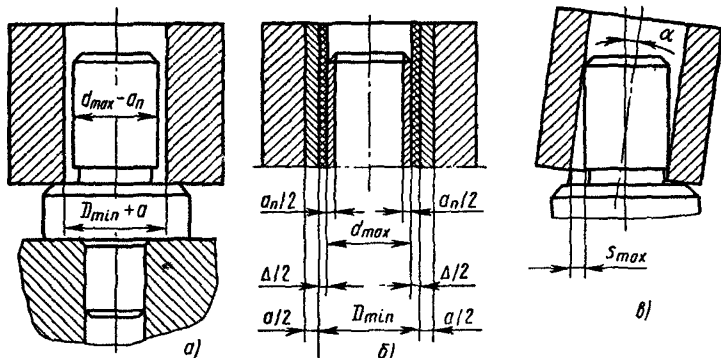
Схема базирования заготовки с главной базой, имеющей форму цилиндрического отверстия:
